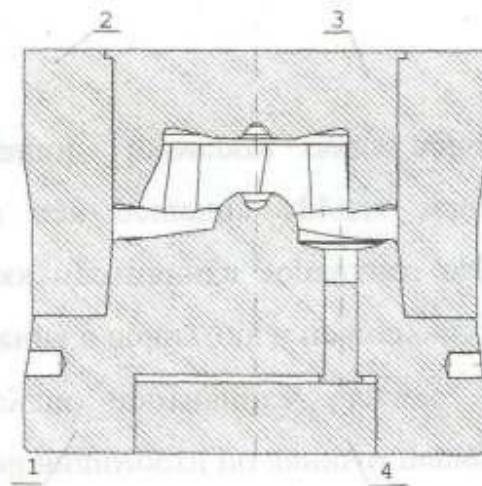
Схема штампа для объемной штамповки стального корпуса фурмы: 1-матрица; 2-обойма; 3-пуансон; 4-выталкиватель
